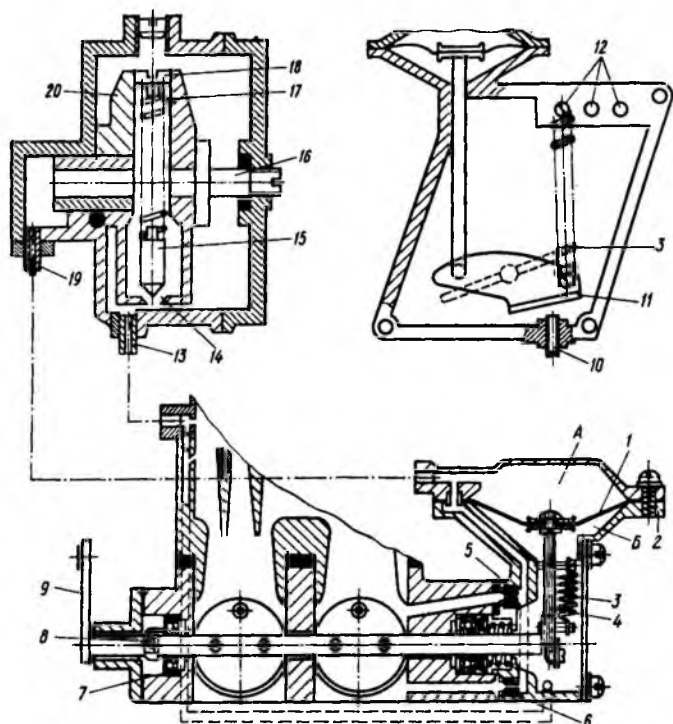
Схема пневмоцентробежного ограничителя частоты вращения коленчатого вала двигателя:
